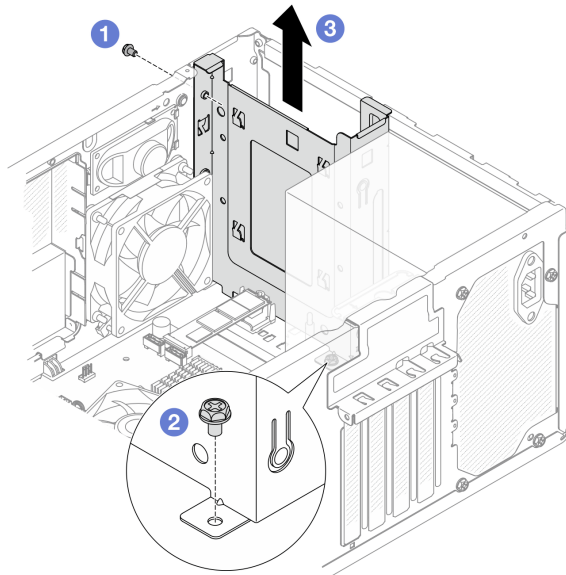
Entfernen der Laufwerkhalterung in Position 0
